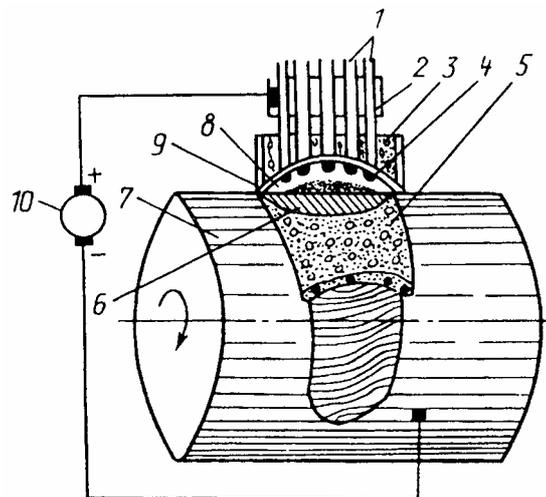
Многоэлектродная наплавка под слоем флюса: 1 – электроды; 2 – токоподводящий контакт; 3 – флюс; 4 – электрическая дуга; 5 – шлаковая корка; 6 – наплавленный металл; 7 – восстанавливаемая деталь; 8 – газопаровой пузырь; 9 – оболочка расплавленного флюса; 10 – источник питания
